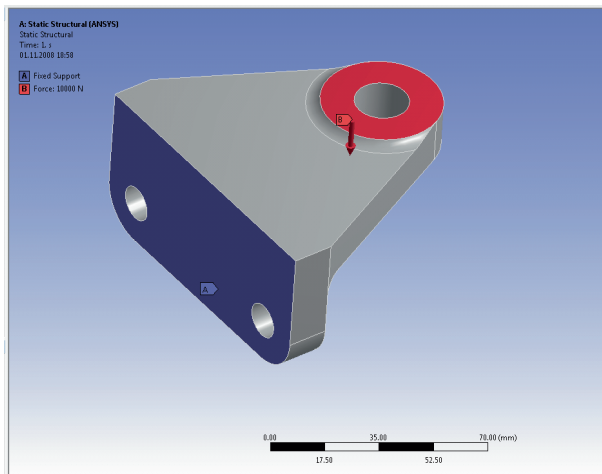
Erste Analyse: Winkelhalter mit Belastung und Lagerung
